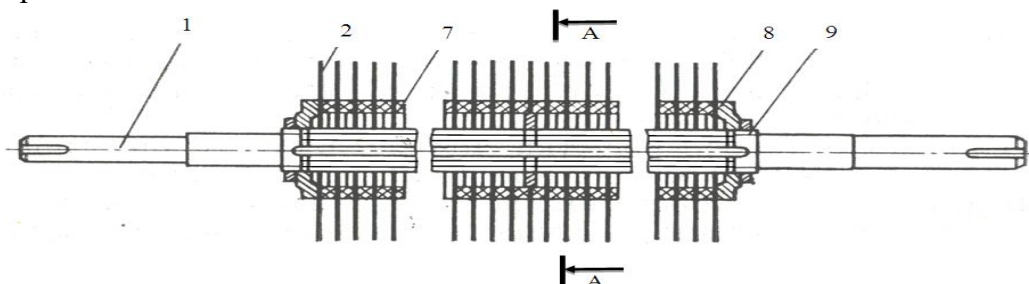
Общий вид новой конструкции пильного цилиндра джина.
